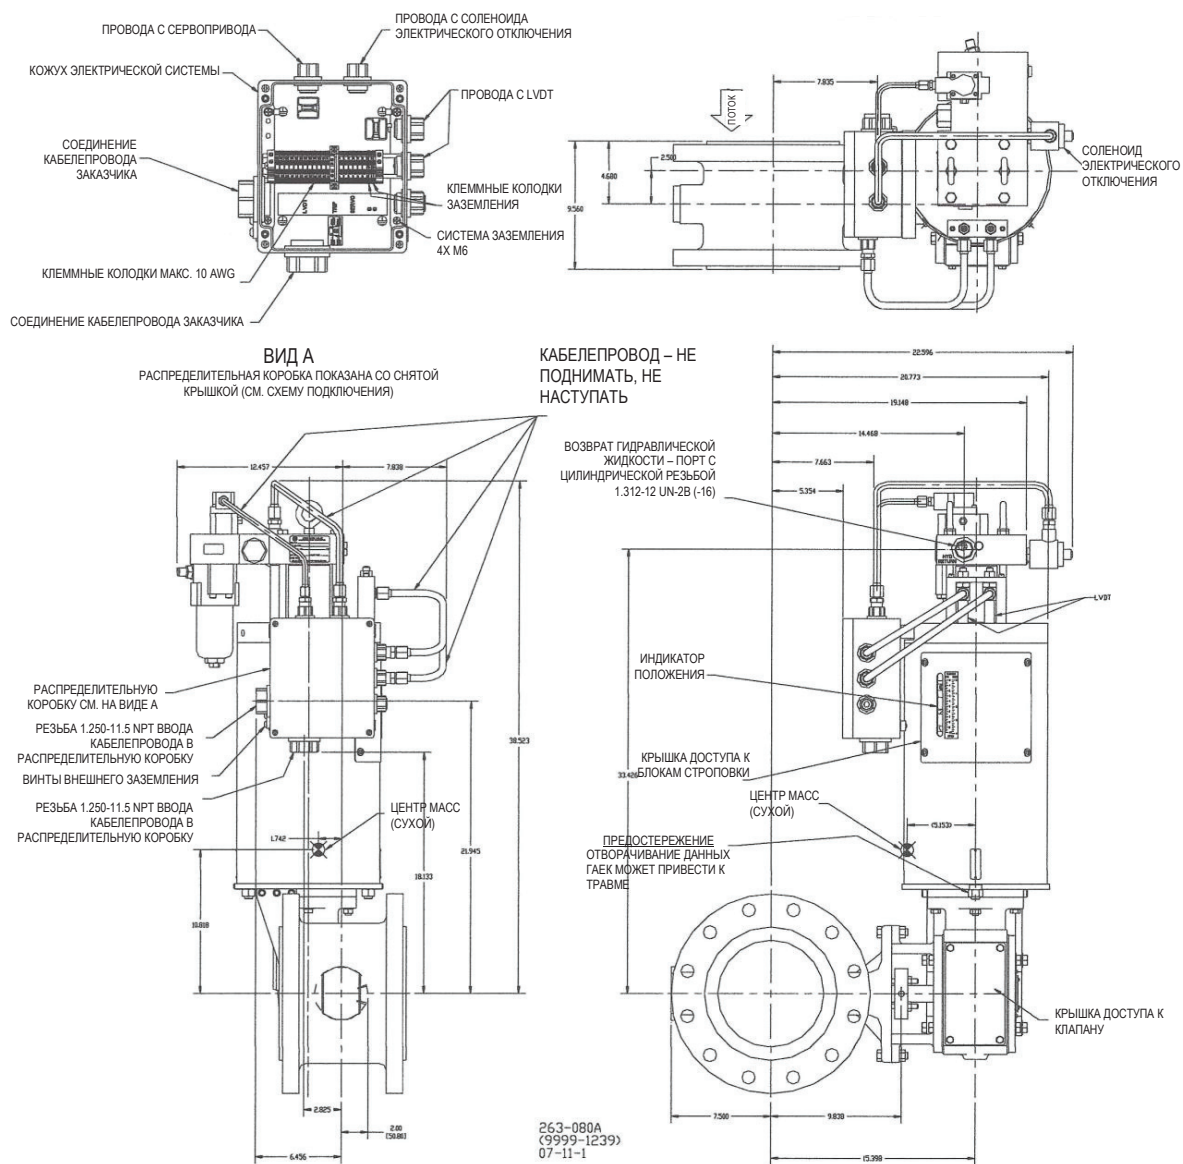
а. Габаритный чертеж 8" запорно-регулирующего газового клапана
